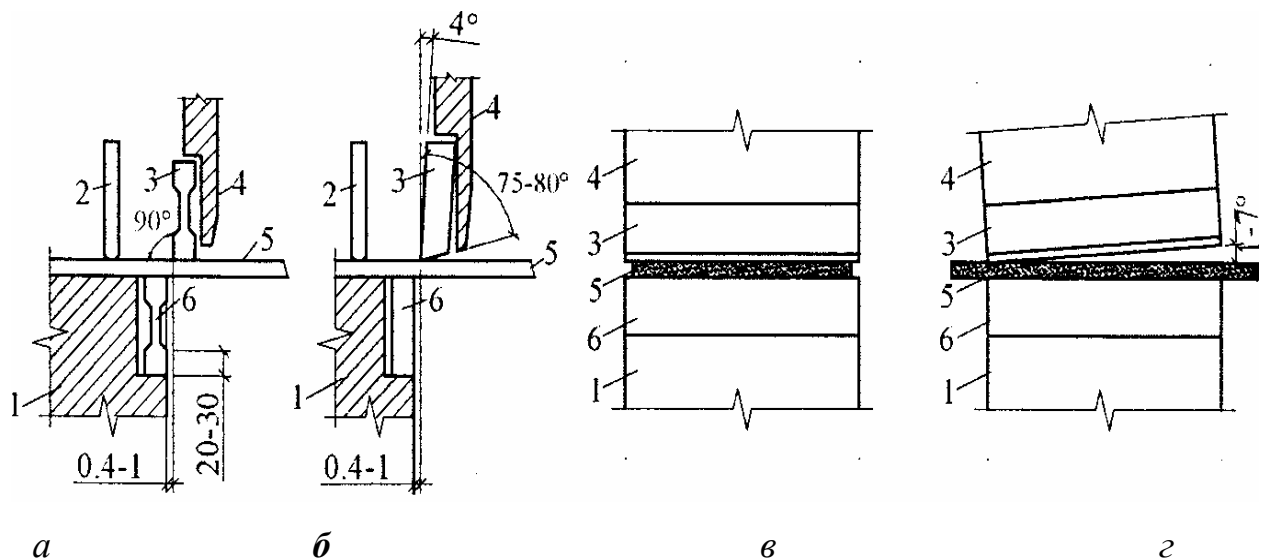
Схема різання листової сталі: а — ножами з пазами; б - похилим ножом; в — прес-ножицями; г - гільйотинними ножицями; 1 - стіл; 2 - притискач; 3 - верхній ніж; 4 - ножова балка; 5 - листова сталь; 6 - нижній ніж
